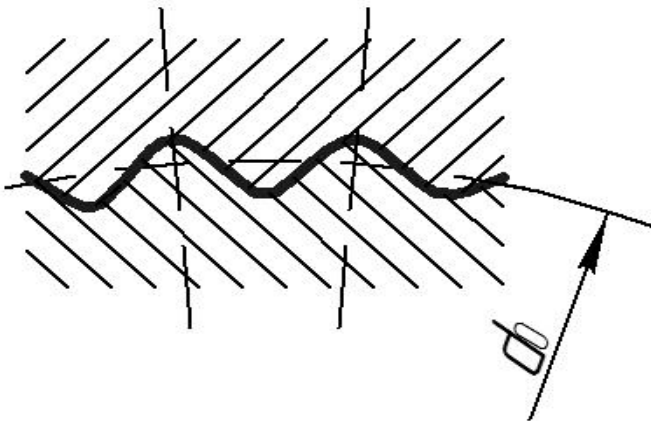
Шліцьове з'єднання з трикутними зубцями
